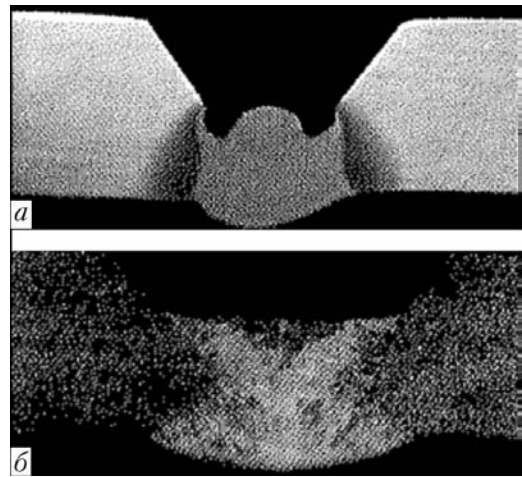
Макрошлиф сварного соединения, выполненного РДС штучными электродами (а) и автоматической сваркой STT (б)
